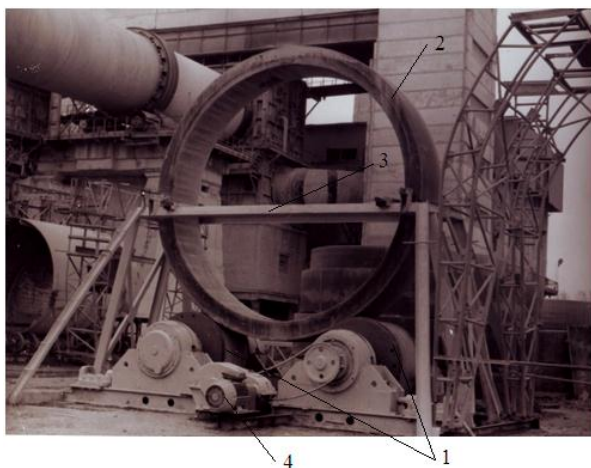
Специальный стенд для обработки поверхностей бандажей
